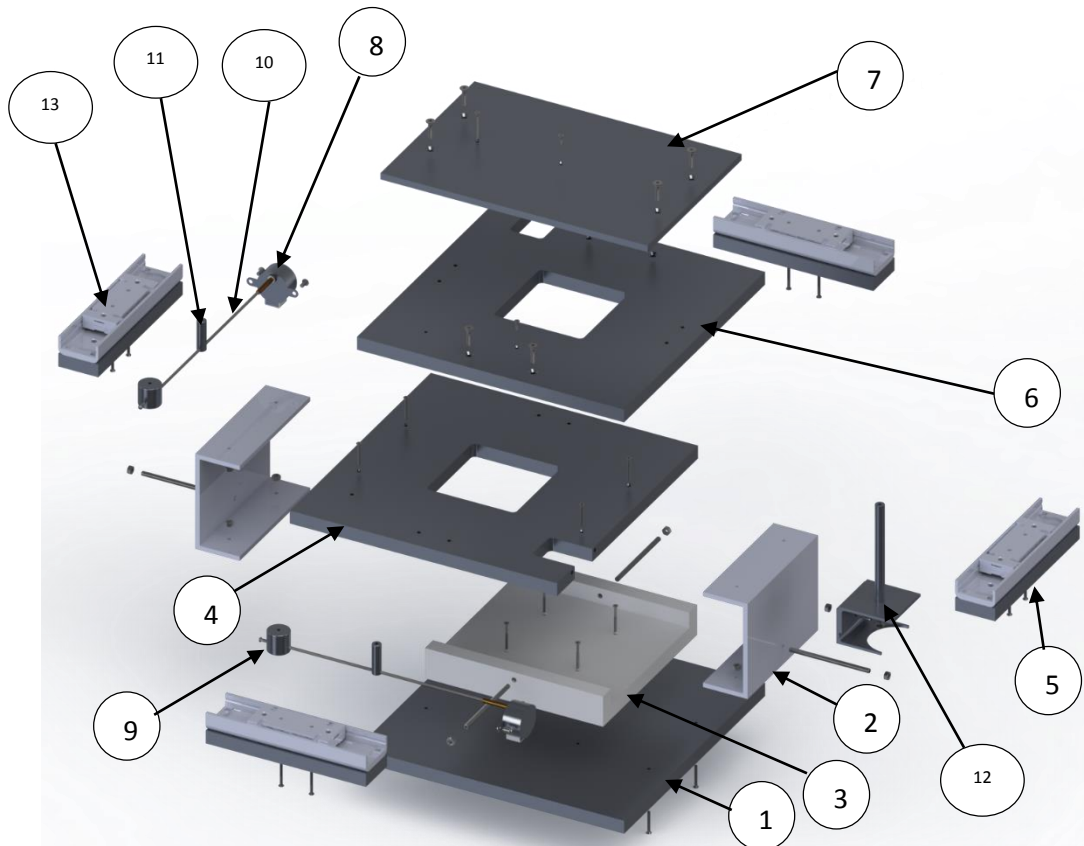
Vista explosionada del sistema de posicionamiento
